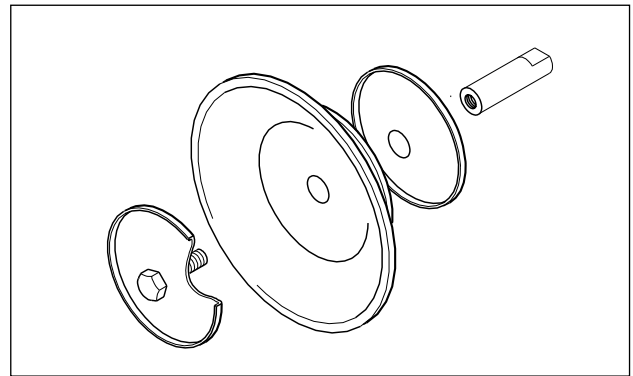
Montage Standardmembran mit Innen- und Außenteller
